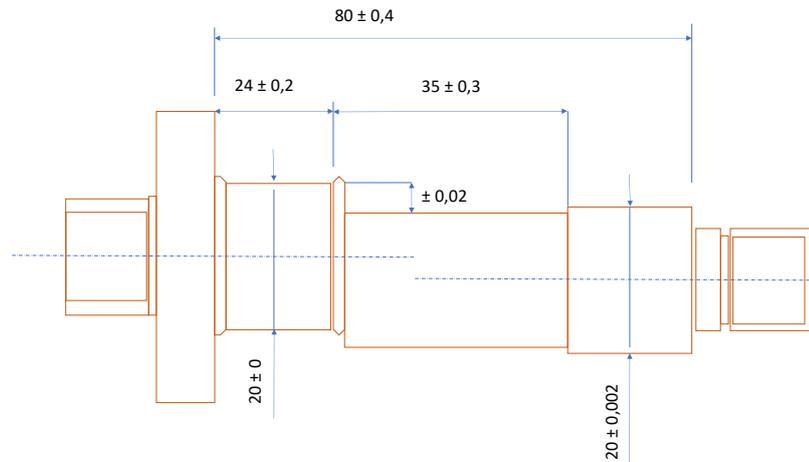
Tolérancement dimensionnel et Alignement des objets
